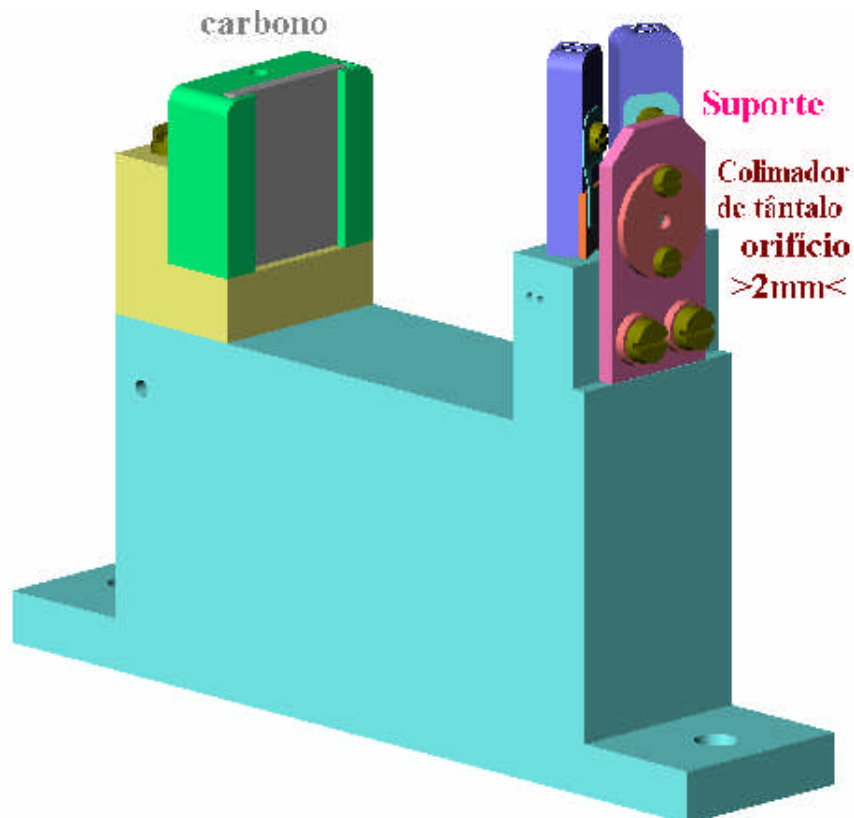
Suporte de amostras utilizado para a implantação de recuo.
